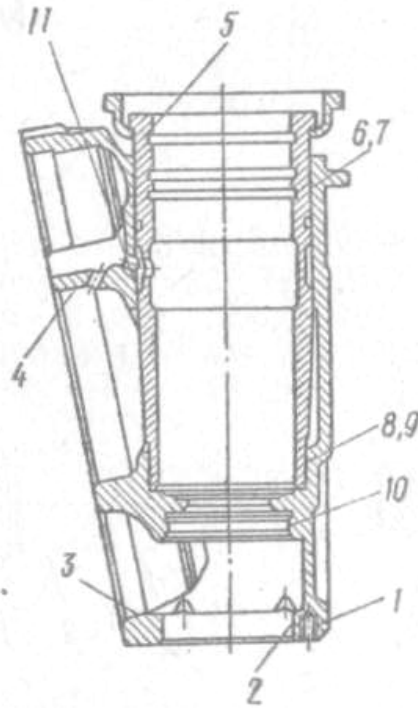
Корпус редуктора з гільзою шкворня в зборі правий 52-2308114-А1, лівий 52-2308115-А1. Матеріал — СЧ 20; маса: гільза — 4,8 кг, корпус — 23,35 кг; твердість: гільза — 170...241 НВ, корпус— 170...241 НВ. Схема дефектів.
